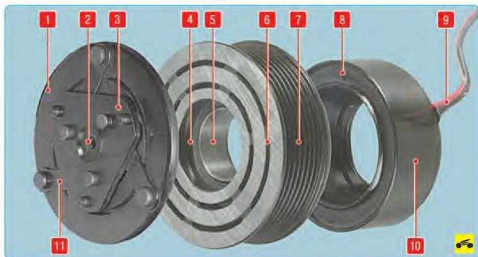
Электромагнитная муфта привода компрессора: 1 – прижимной диск муфты; 2 – шлицевое отверстие ступицы диска; 3 – ведомый диск муфты; 4 – подшипник; 5 – внутренняя обойма подшипника; 6 – рабочая поверхность шкива; 7 – ручки шкива; 8 – обмотка электромагнита; 9 – жгут проводов электромагнита; 10 – корпус электромагнита; 11 – упругий стальной поводок
